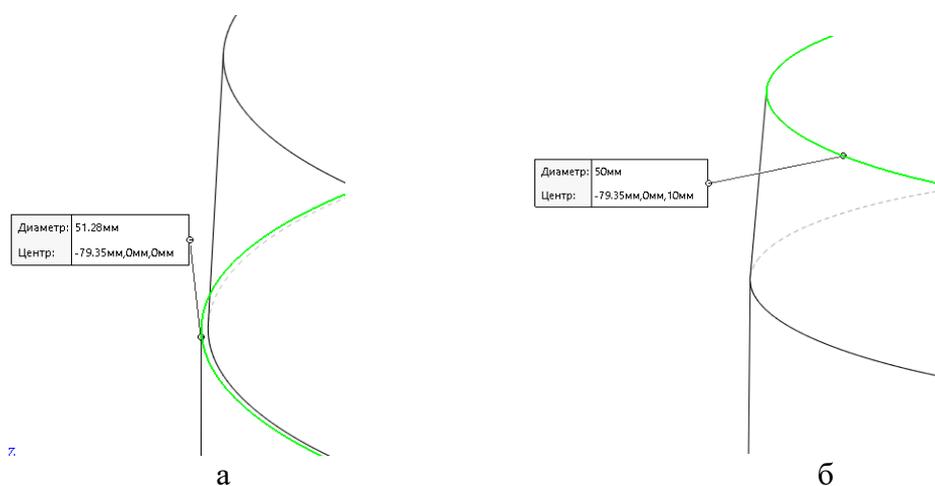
Поверхность разъема с изломом (а) и без излома (б)
